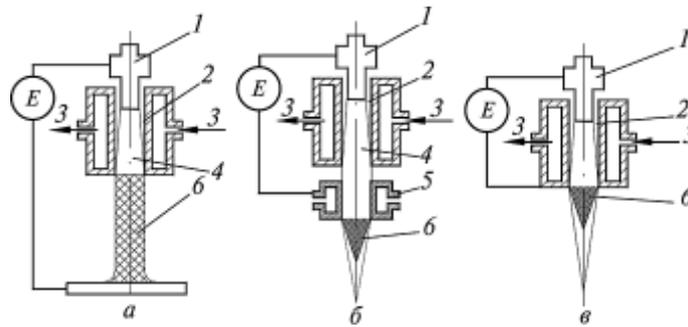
Схемы процесса плазменной сварки плазменной дугой (а) и плазменной струей (б, в):
